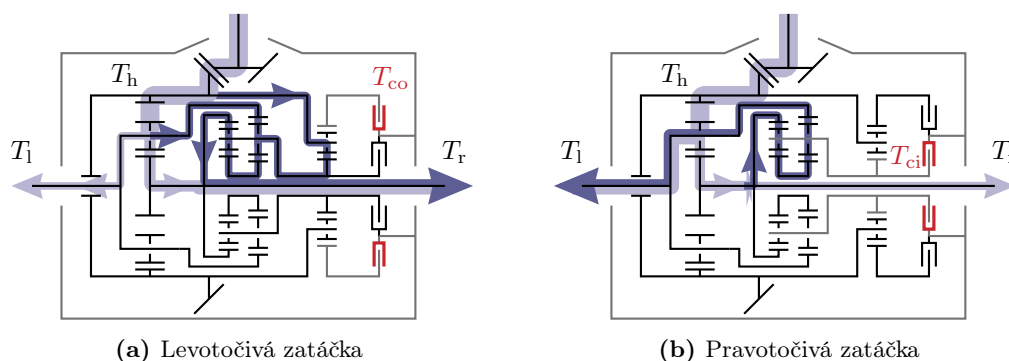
Zatížení ozubených kol u dvou různých konstrukcí
